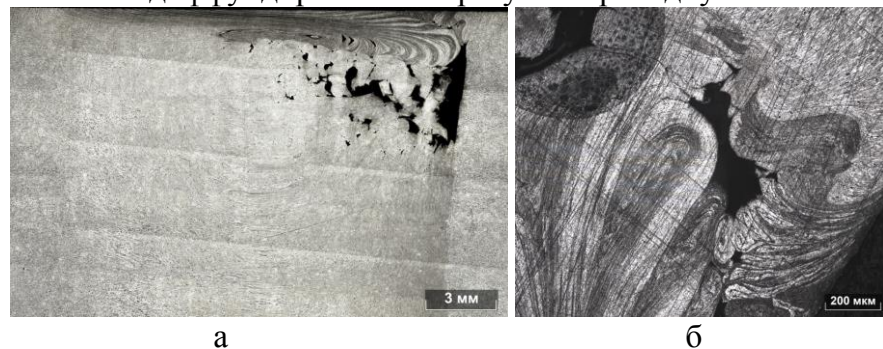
Внешний вид сварного соединения: а) с дефектом; б) фрагмент подповерхностной зоны
